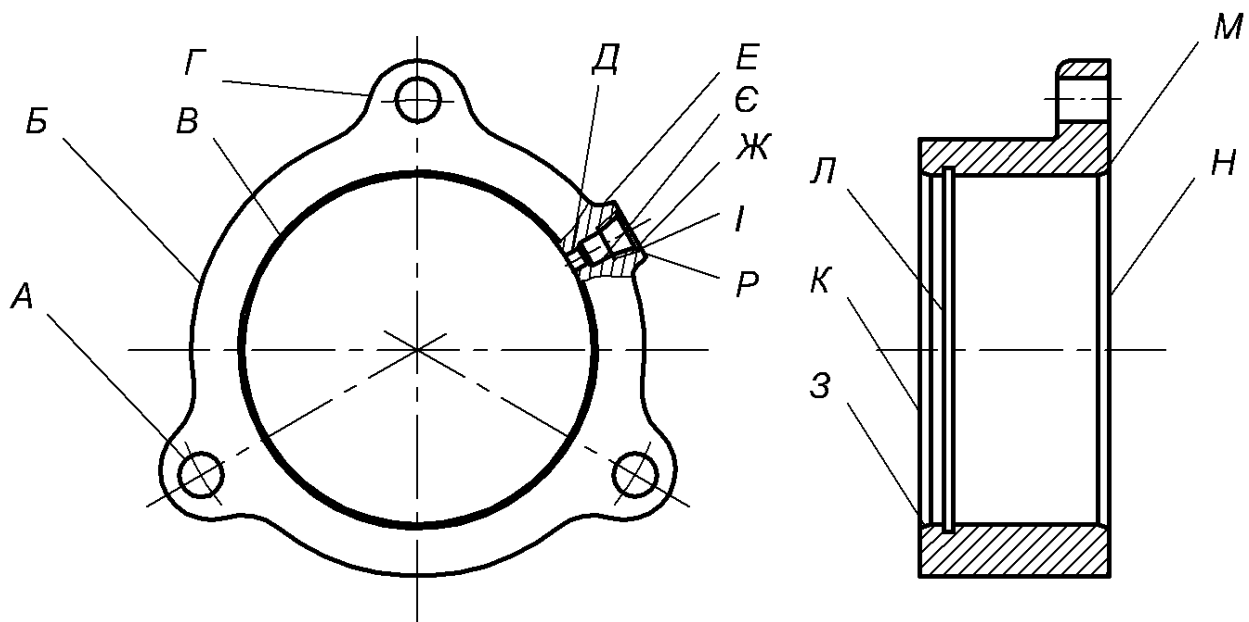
Позначення поверхонь корпуса підшипника
